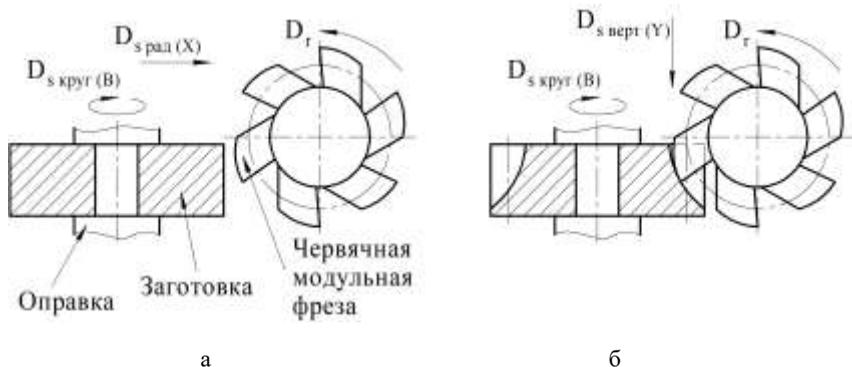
Формообразующие движения зубофрезерного станка:
